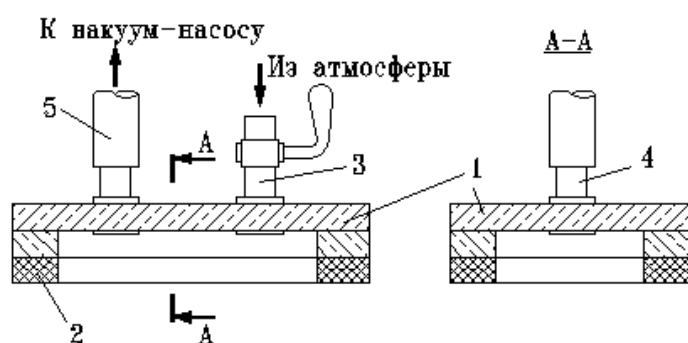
Вакуум-камера плоская для испытания герметичности сварных швов: 1 – корпус из оргстекла; 2 – губчатая резина; 3 – кран; 4 – патрубок; 5 – шланг
